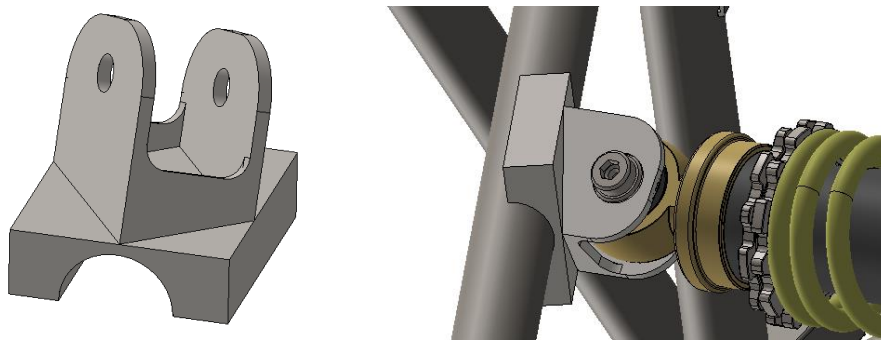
Diseño del soporte del balancín trasero
